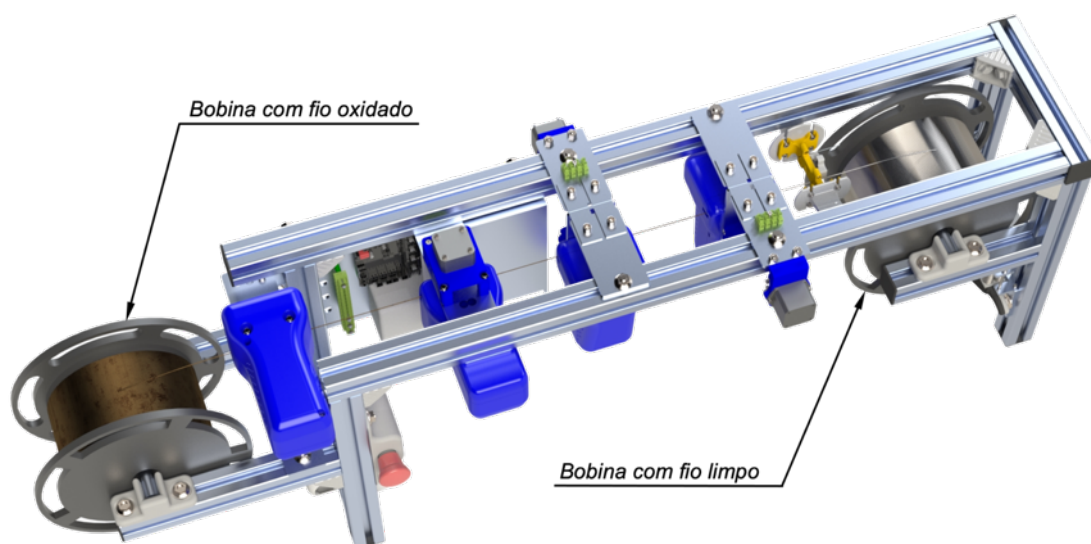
Representação da adaptação de bancada denominada por EROI V2-B, onde existe a transferência do fio de soldadura de uma bobina para outra, sendo efetuada a limpeza e a inspeção por CI do fio de soldadura.
